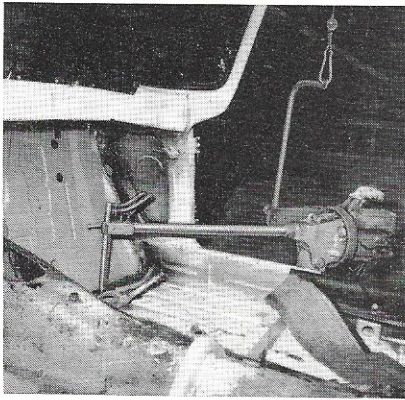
Soudage tôle de tablier plancher de pédales sur plancher avant. Pince ARO. - Porte-électrodes 107478.
